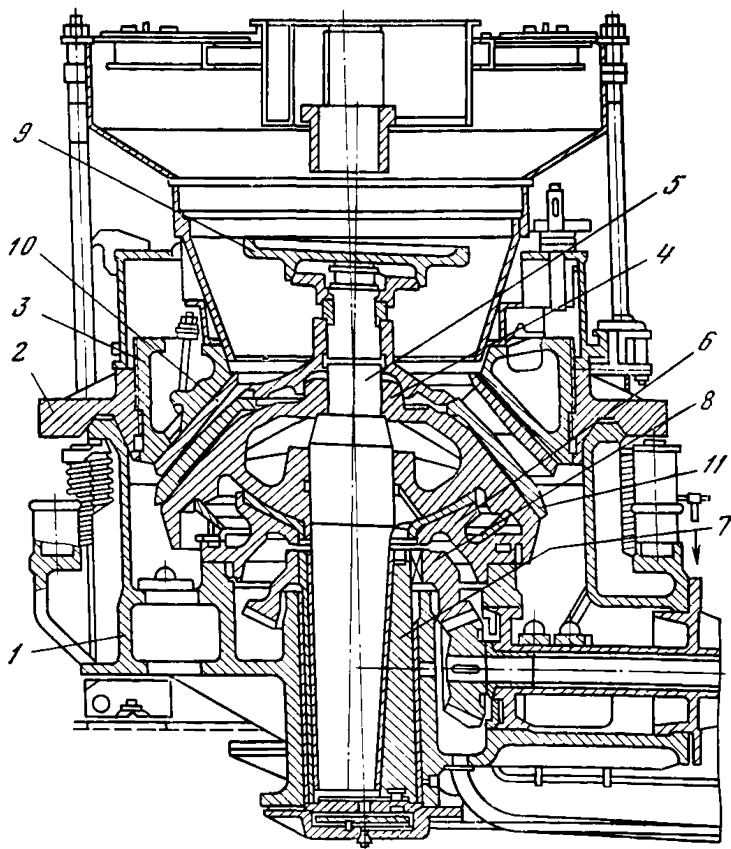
Дробилка конусная среднего и мелкого дробления:
